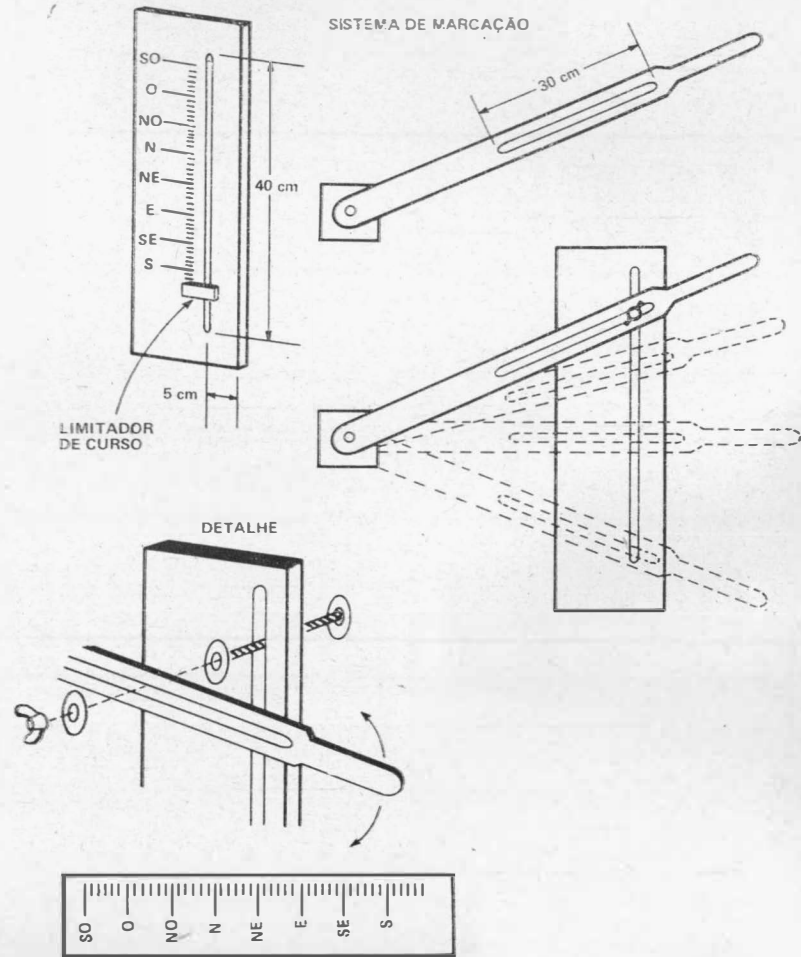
Detalhes da alavanca de posicionamento, sistema de fixação e marcador de posição do rotor manual de antenas.
